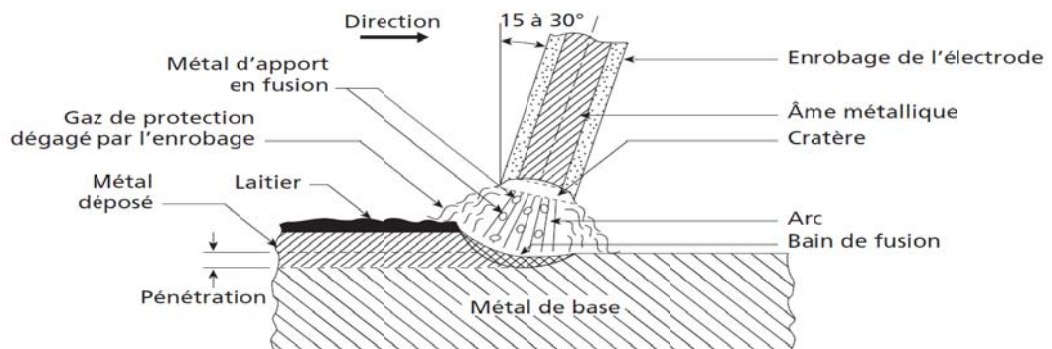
Principe de soudage à l'arc avec électrode enrobée (SMAW) [23]
